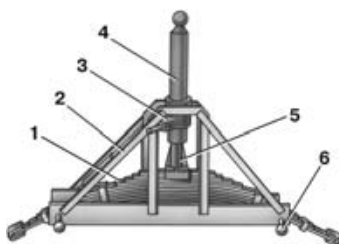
Приспособление для установки рессор на автомобилях семейства УАЗ-3741: 1 - рессора; 2 - рама; 3 - рычаг; 4 - обойма винта; 5 - головка; 6 - чека.
